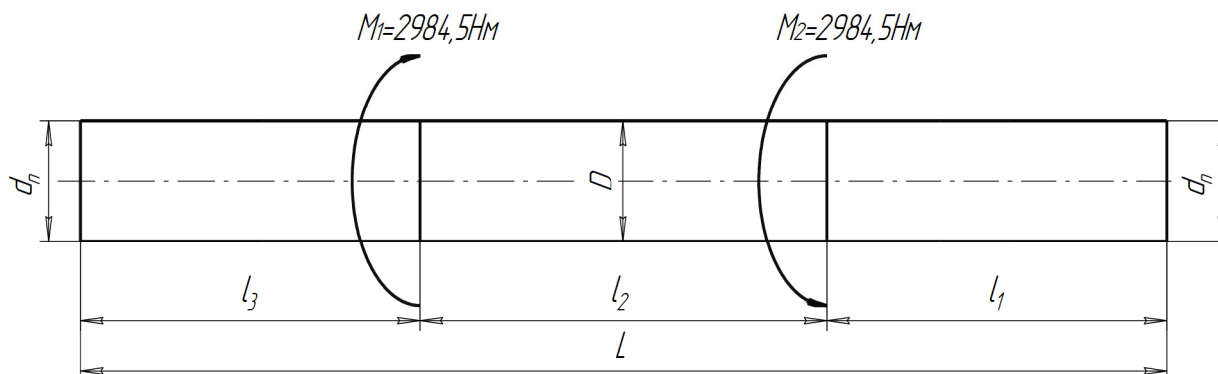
Кінематична схема проміжного вала механізму підйому грейфера
